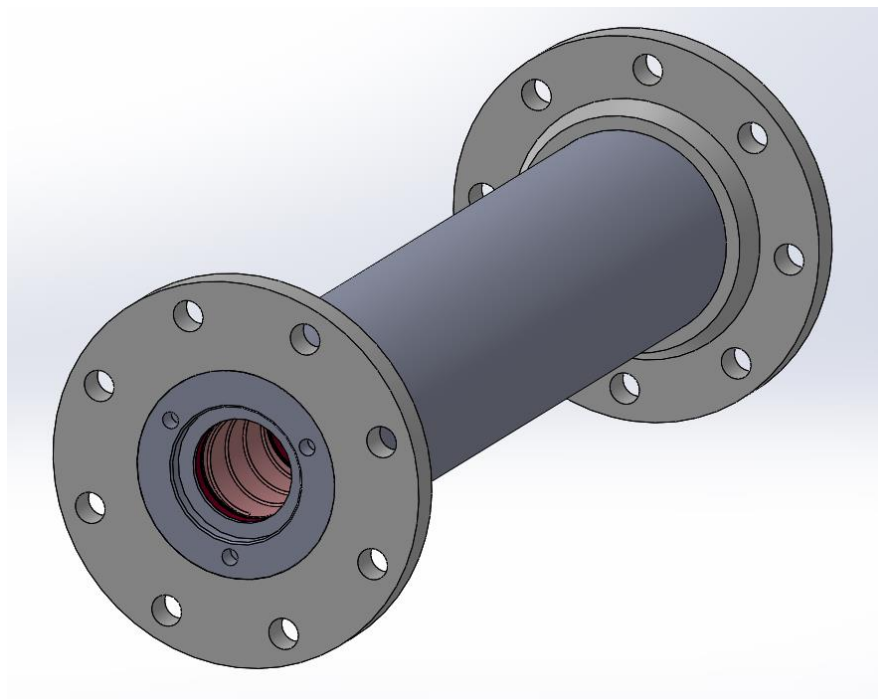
Модель модернізованої конструкції корпусу
